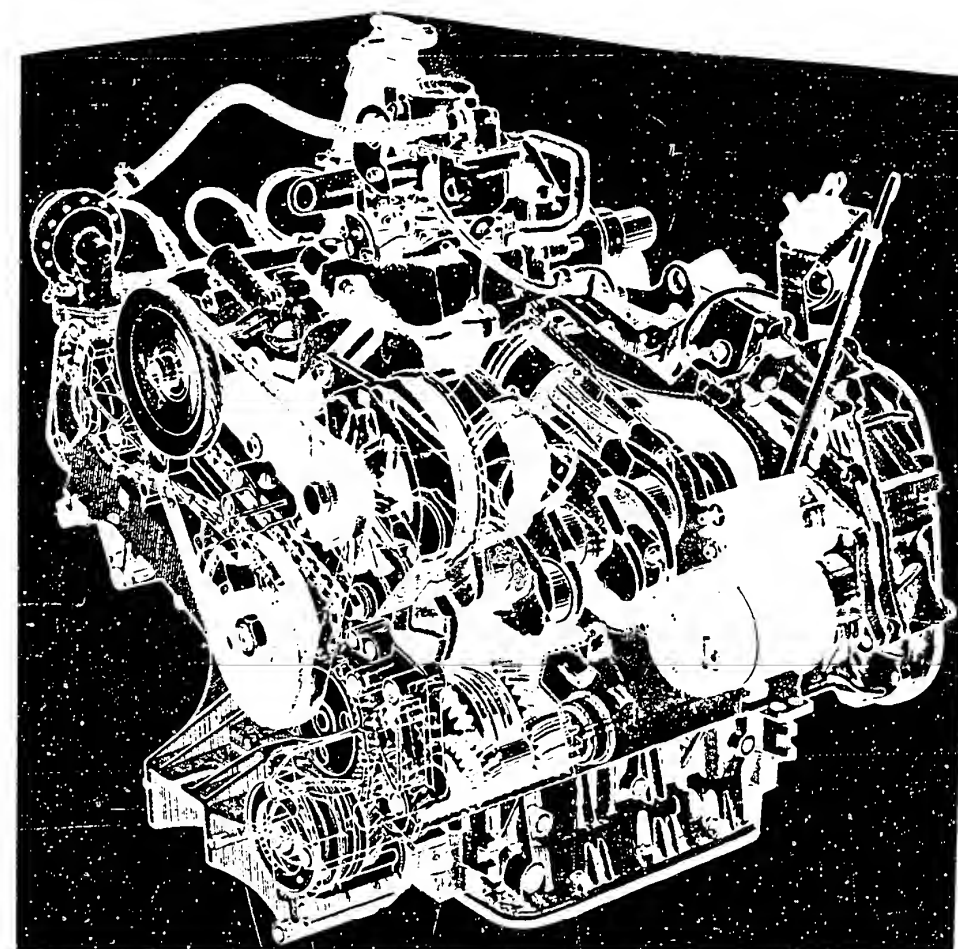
Der fast liegend eingebaute 1,1 und 1,3l Motor teilweise geschnitten. Man erkennt das in der Ölwanne eingebaute Getriebe.
